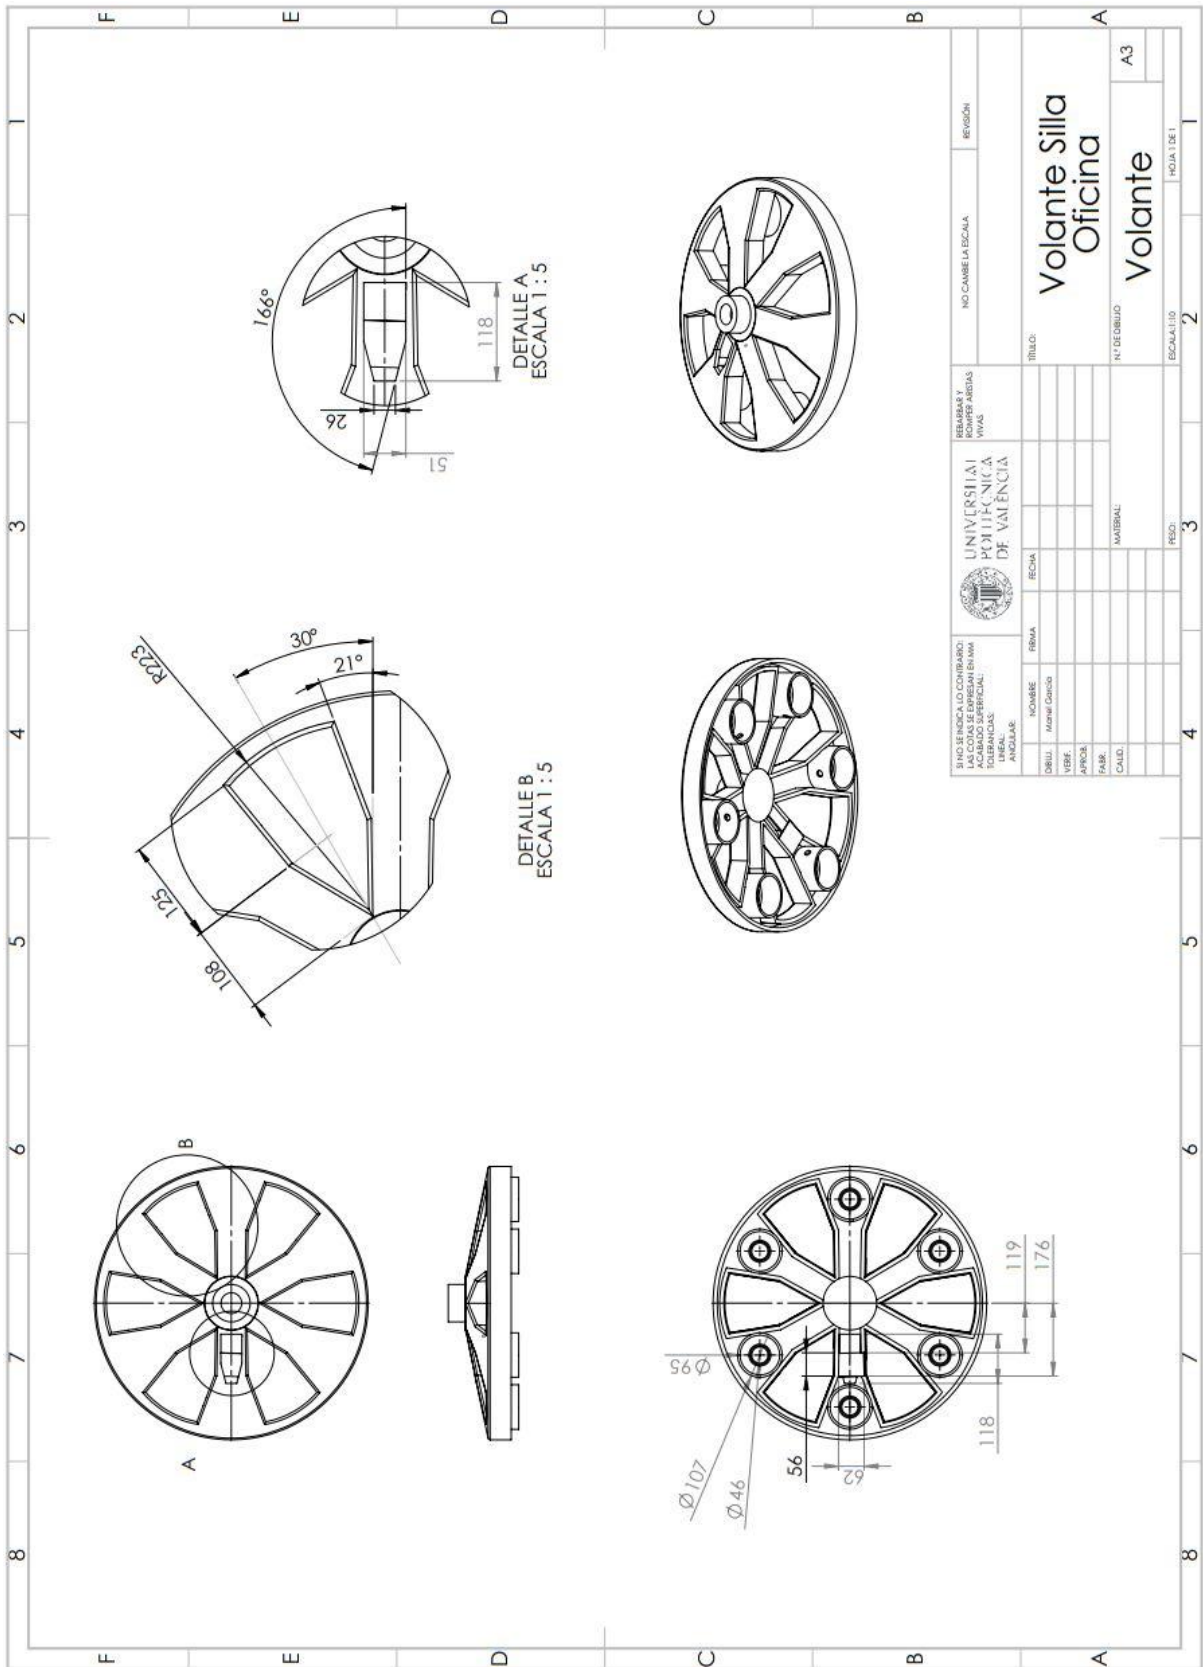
Planimetría silla Maadapt. Fuente: Elaboración propia (2018).
